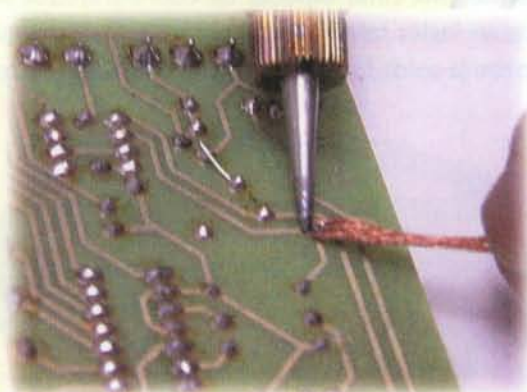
Retirando la soldadura con la cinta de cobre trenzada
